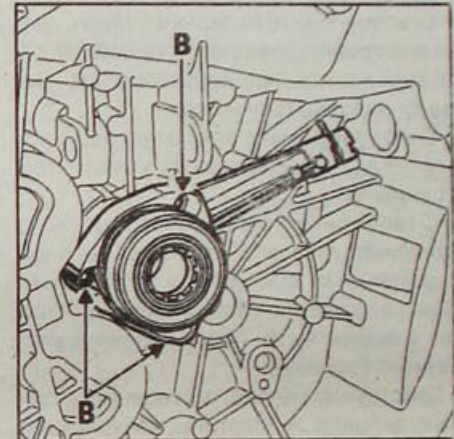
Расположение болтов (В) крепления рабочего цилиндра сцепления
